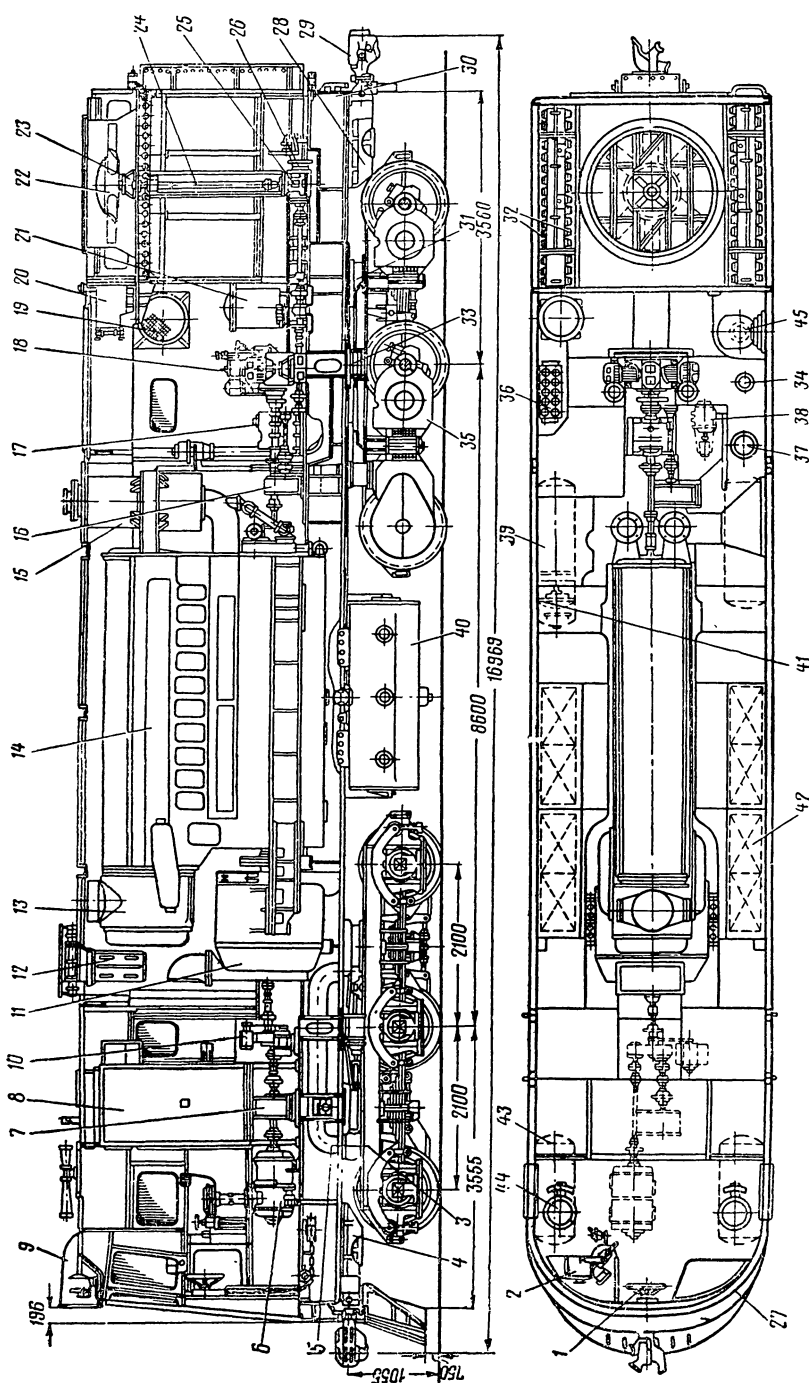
Продольный разрез и план тепловоза ТЭЗ:
